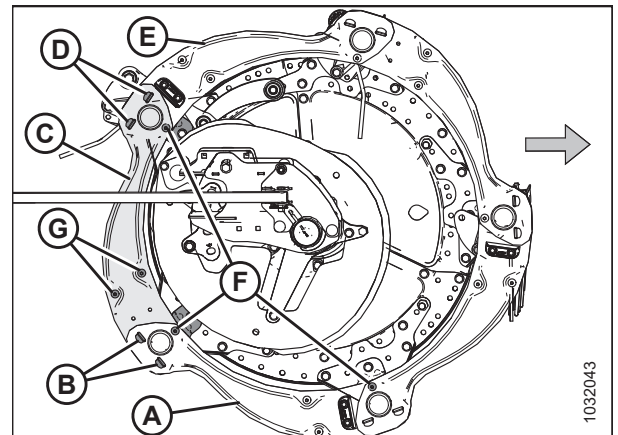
Бокові щитки мотовила — зовнішній кінець ексцентрика
